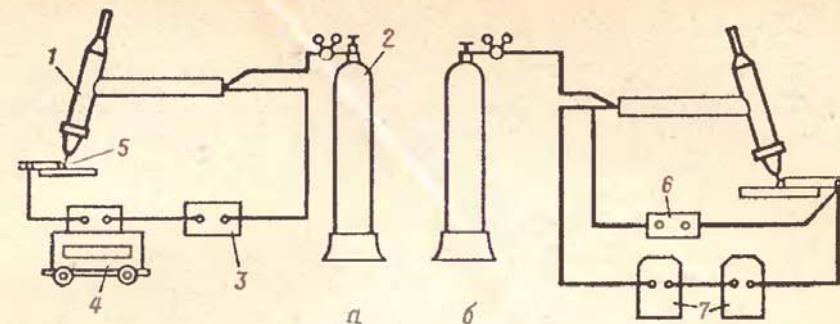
Схема (упрощенная) ручной аргонодуговой сварки постоянным (а) и переменным (б) током:
